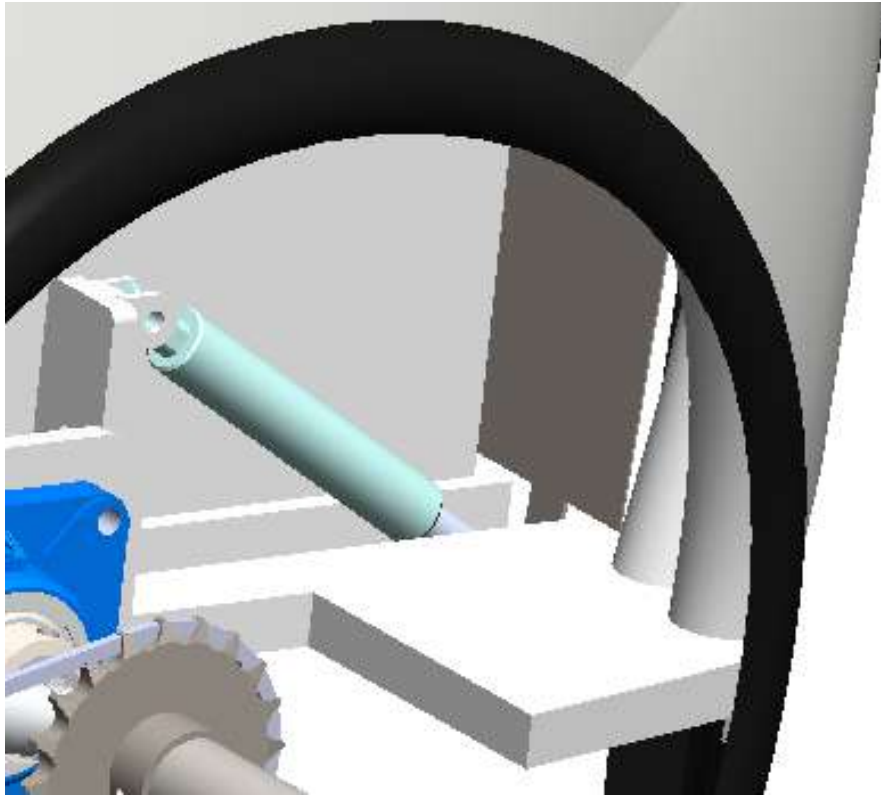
Sistema de apertura de puerta inferior con pistón de elevación. Fuente: (Vaca, José, 2018)
